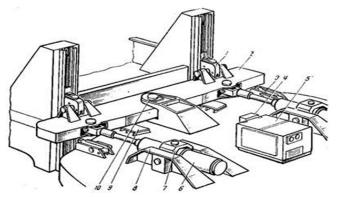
Изгибающее устройство с поворотной балкой: 1 – автосцеп УДР; 2 – поворотная балка; 3 – фиксатор нейтрального положения; 4 – станция управления; 5 – насосная станция: 6 – гидроцилиндр; 7 – карданный подвес; 8, 9 – опоры гидроцилиндра и поворотной балки; 10 – кронштейн центральной оси поворота
